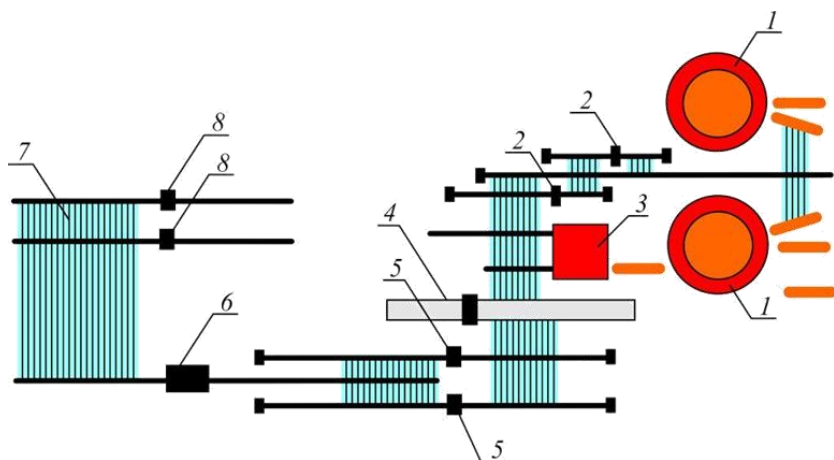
Трубопрокатный агрегат ТПА 400:
